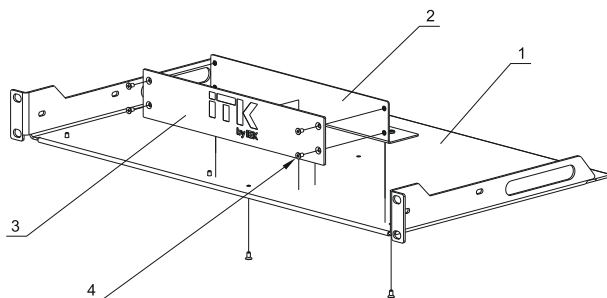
Сборка изделия / Figure 2 – Product assembly / 2 сурет – Бұйымды құрастыру
